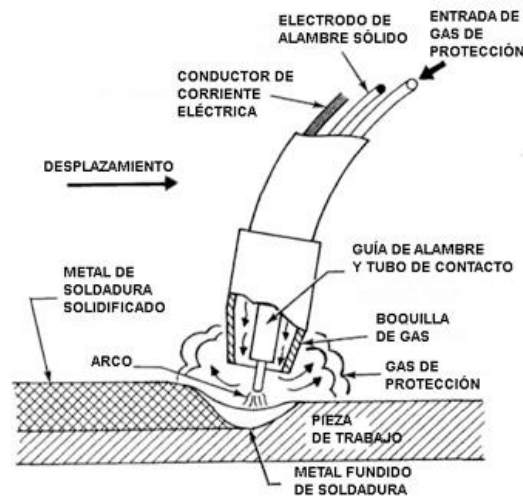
Proceso de soldadura MIG. [18]
